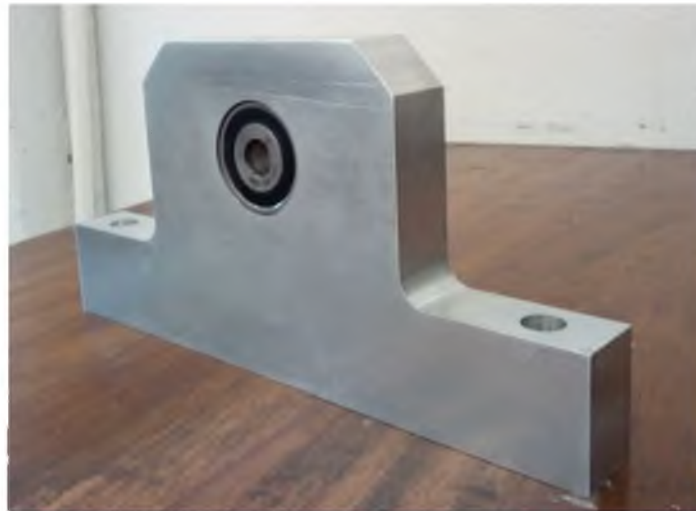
Rodamiento *SKF* 6301 montado en la chumacera manufacturada.
